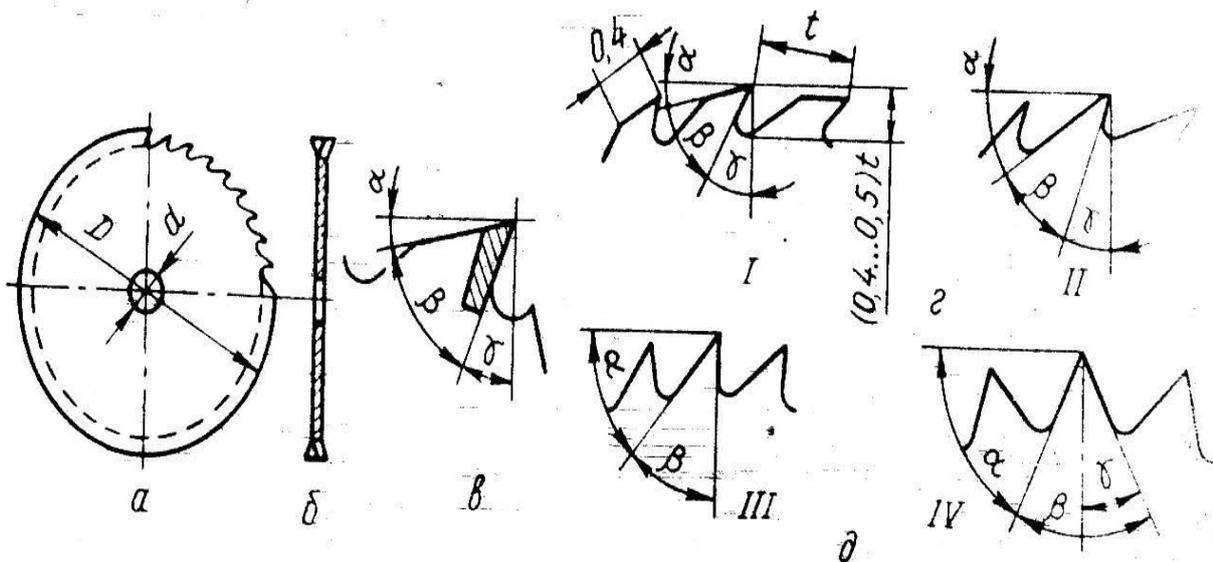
Круглые плоские пилы: а, б – общий вид; в – зуб пилы с пластинкой ТСП; г – тип 1 (профиль I, II); д – тип 2 (профиль III, IV).
